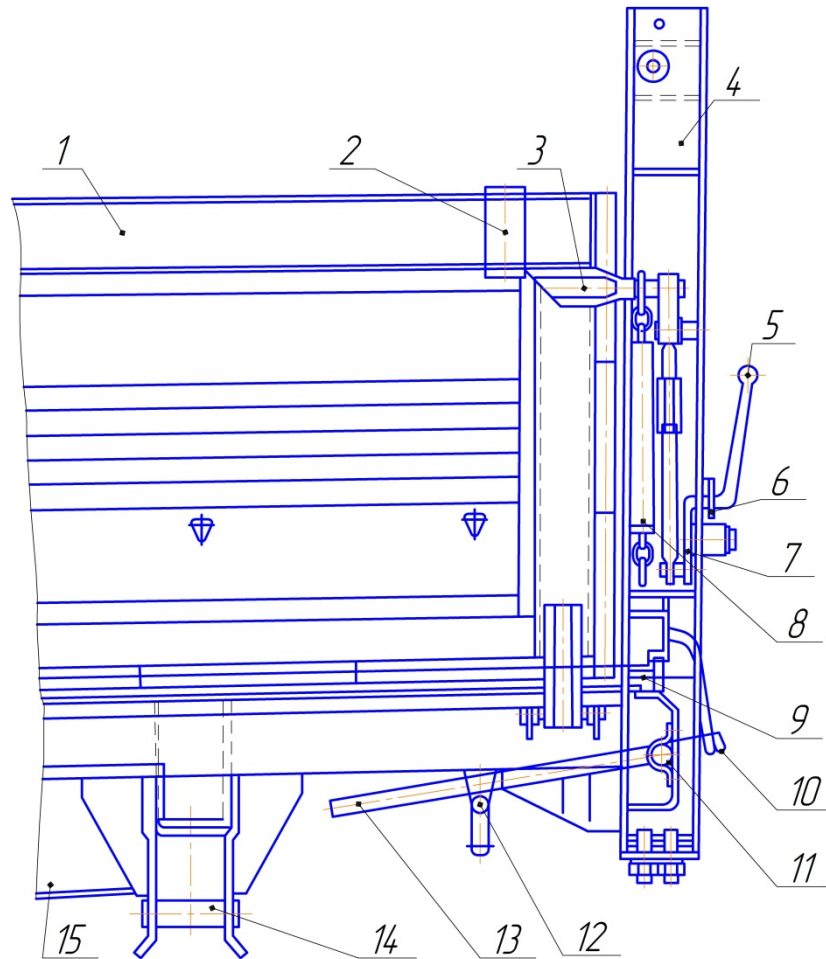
Механізм закривання борта автомобіля MAN TGE: 1 – бічний борт; 2 – гніздо стійки додаткового борта; 3 – цапфа закривачів бічних бортів; 4 – стійка навішувача заднього борта; 5 – рукоятка важеля механізму закривання бічних бортів; 6 – фіксатор механізму закривання бічних бортів; 7 – важіль механізму закривання бічних бортів; 8 – ланцюги; 9 – горизонтальний ущільнювач заднього борта; 10 – закривач заднього борта; 11 – вал закривача заднього борта; 12 – фіксуючий штир; 13 – ручка закривача заднього борта; 14 – опорні шарніри; 15 – основа платформи.
